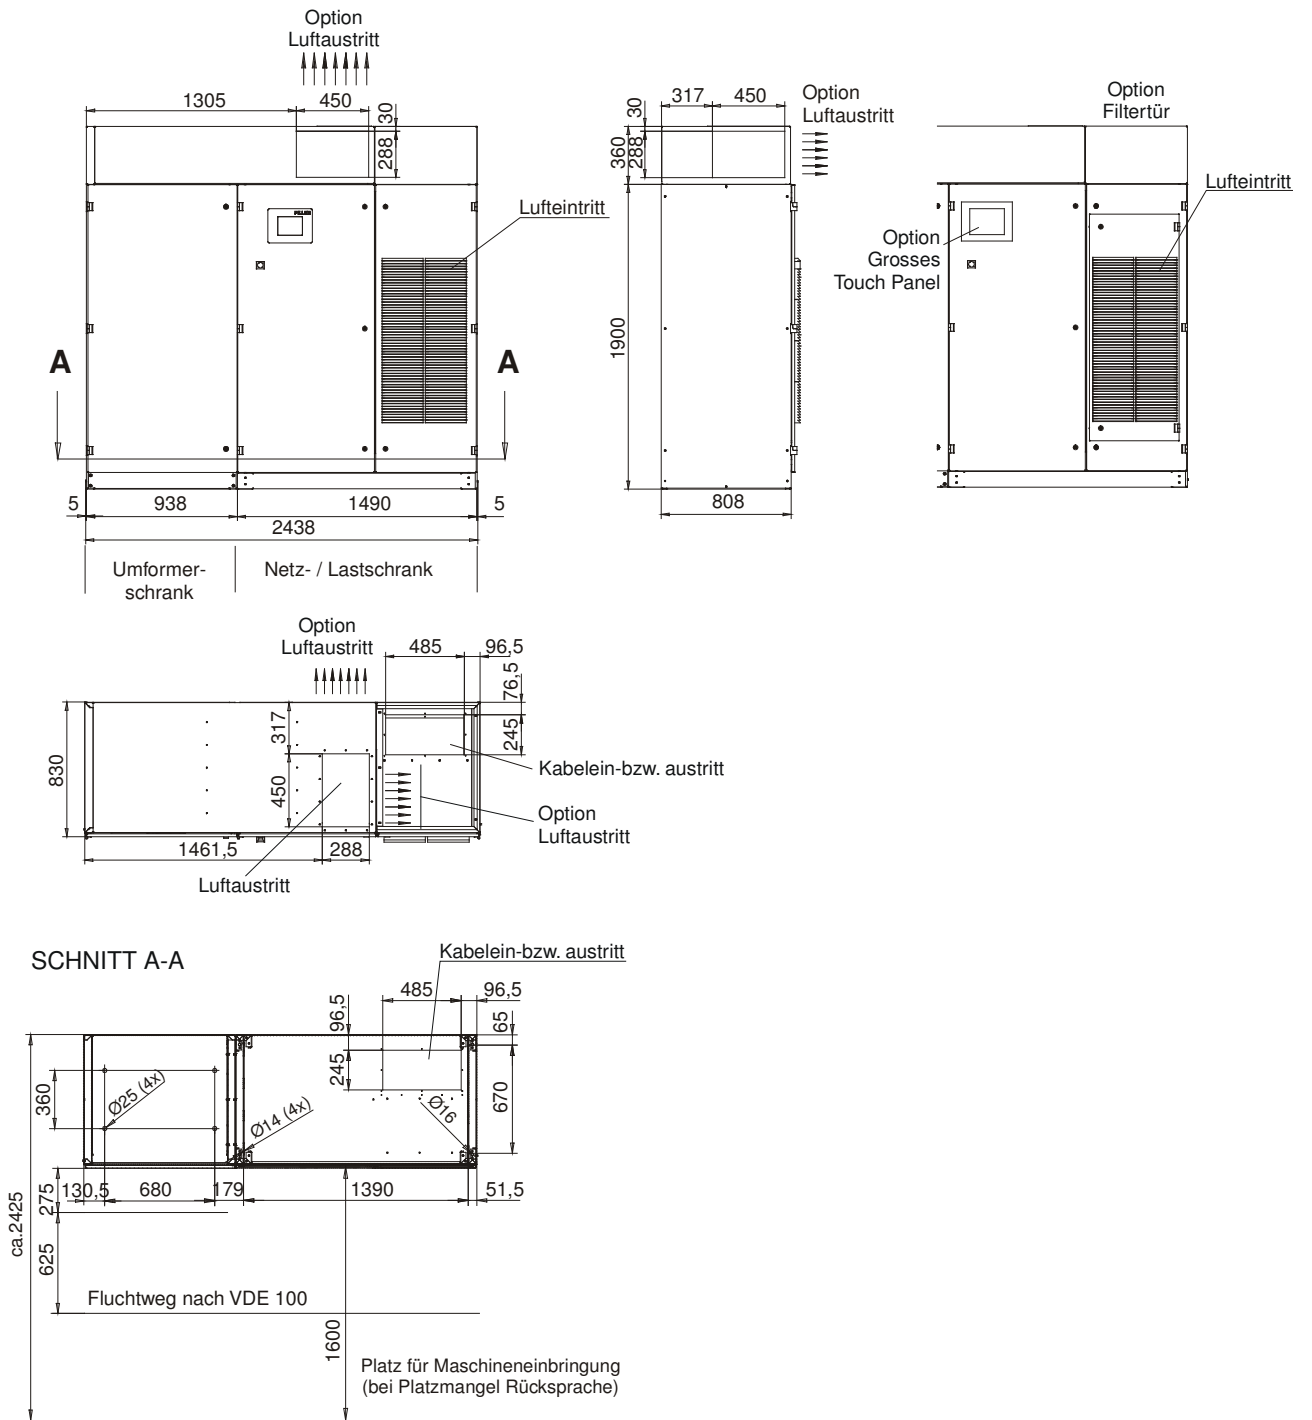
Abmessungen UB220 – UB330 mit Schalldämpfer
